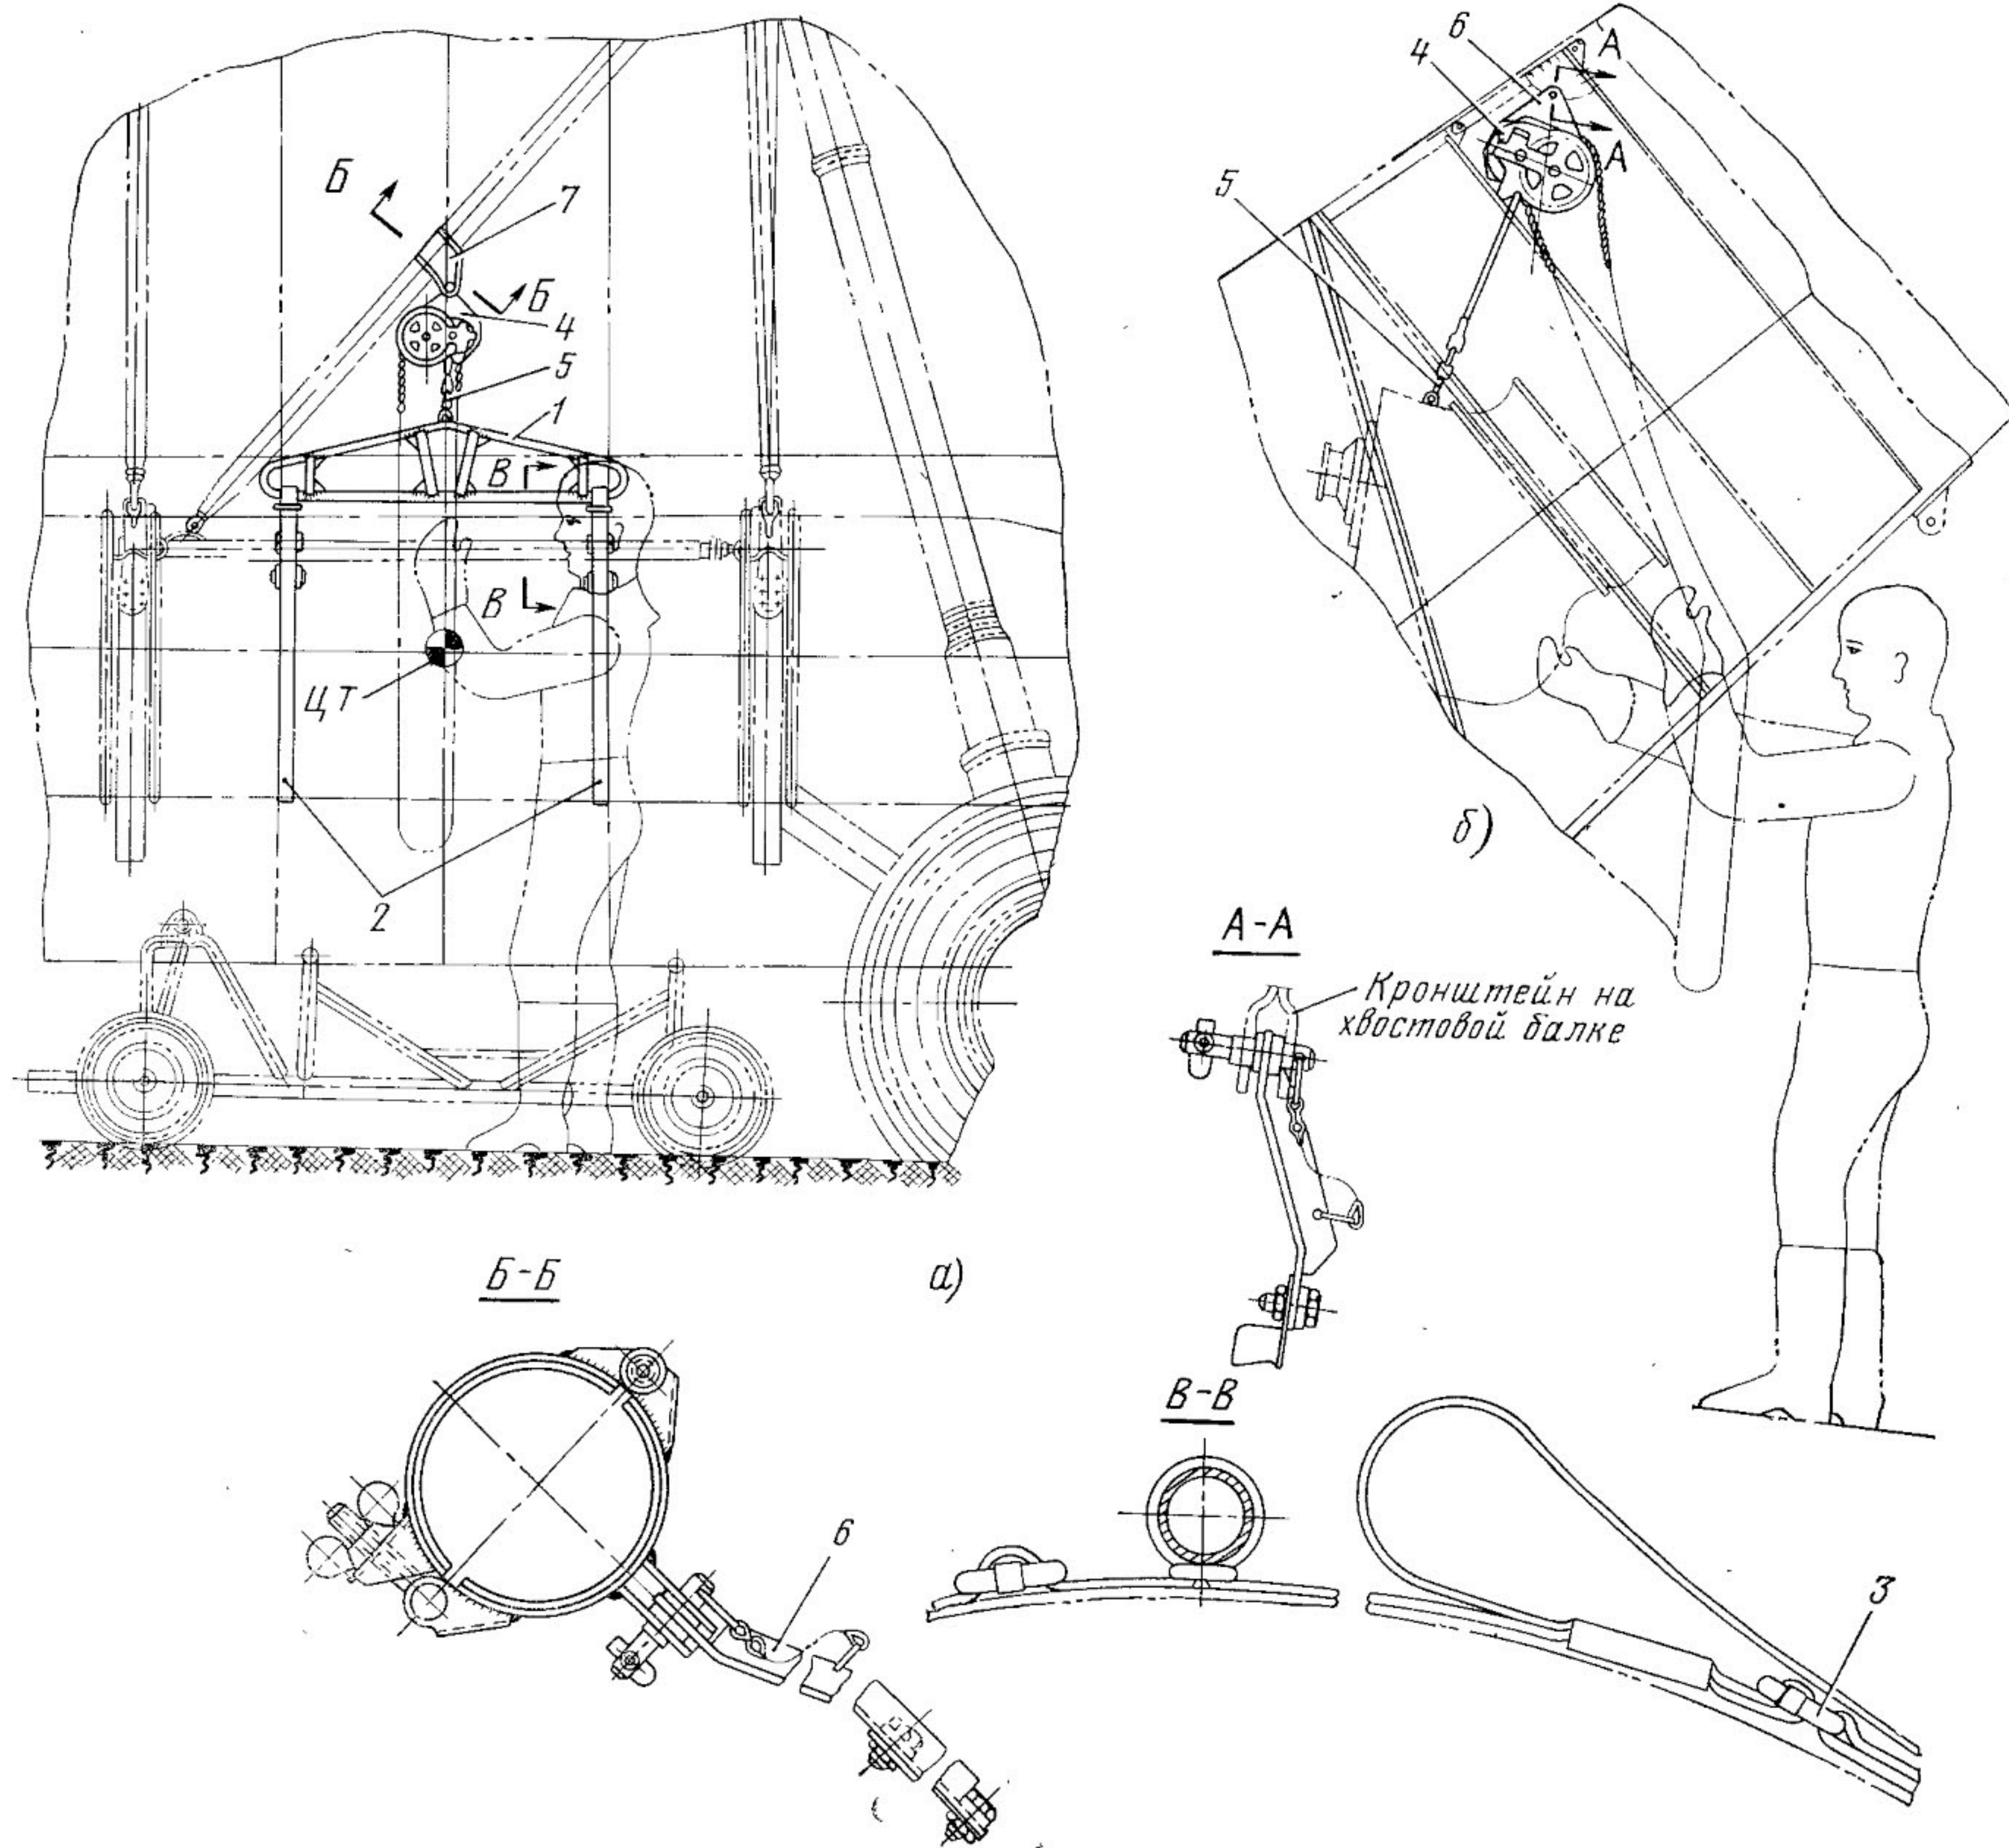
Приспособление для монтажа подвесного бака и промежуточного редуктора:
